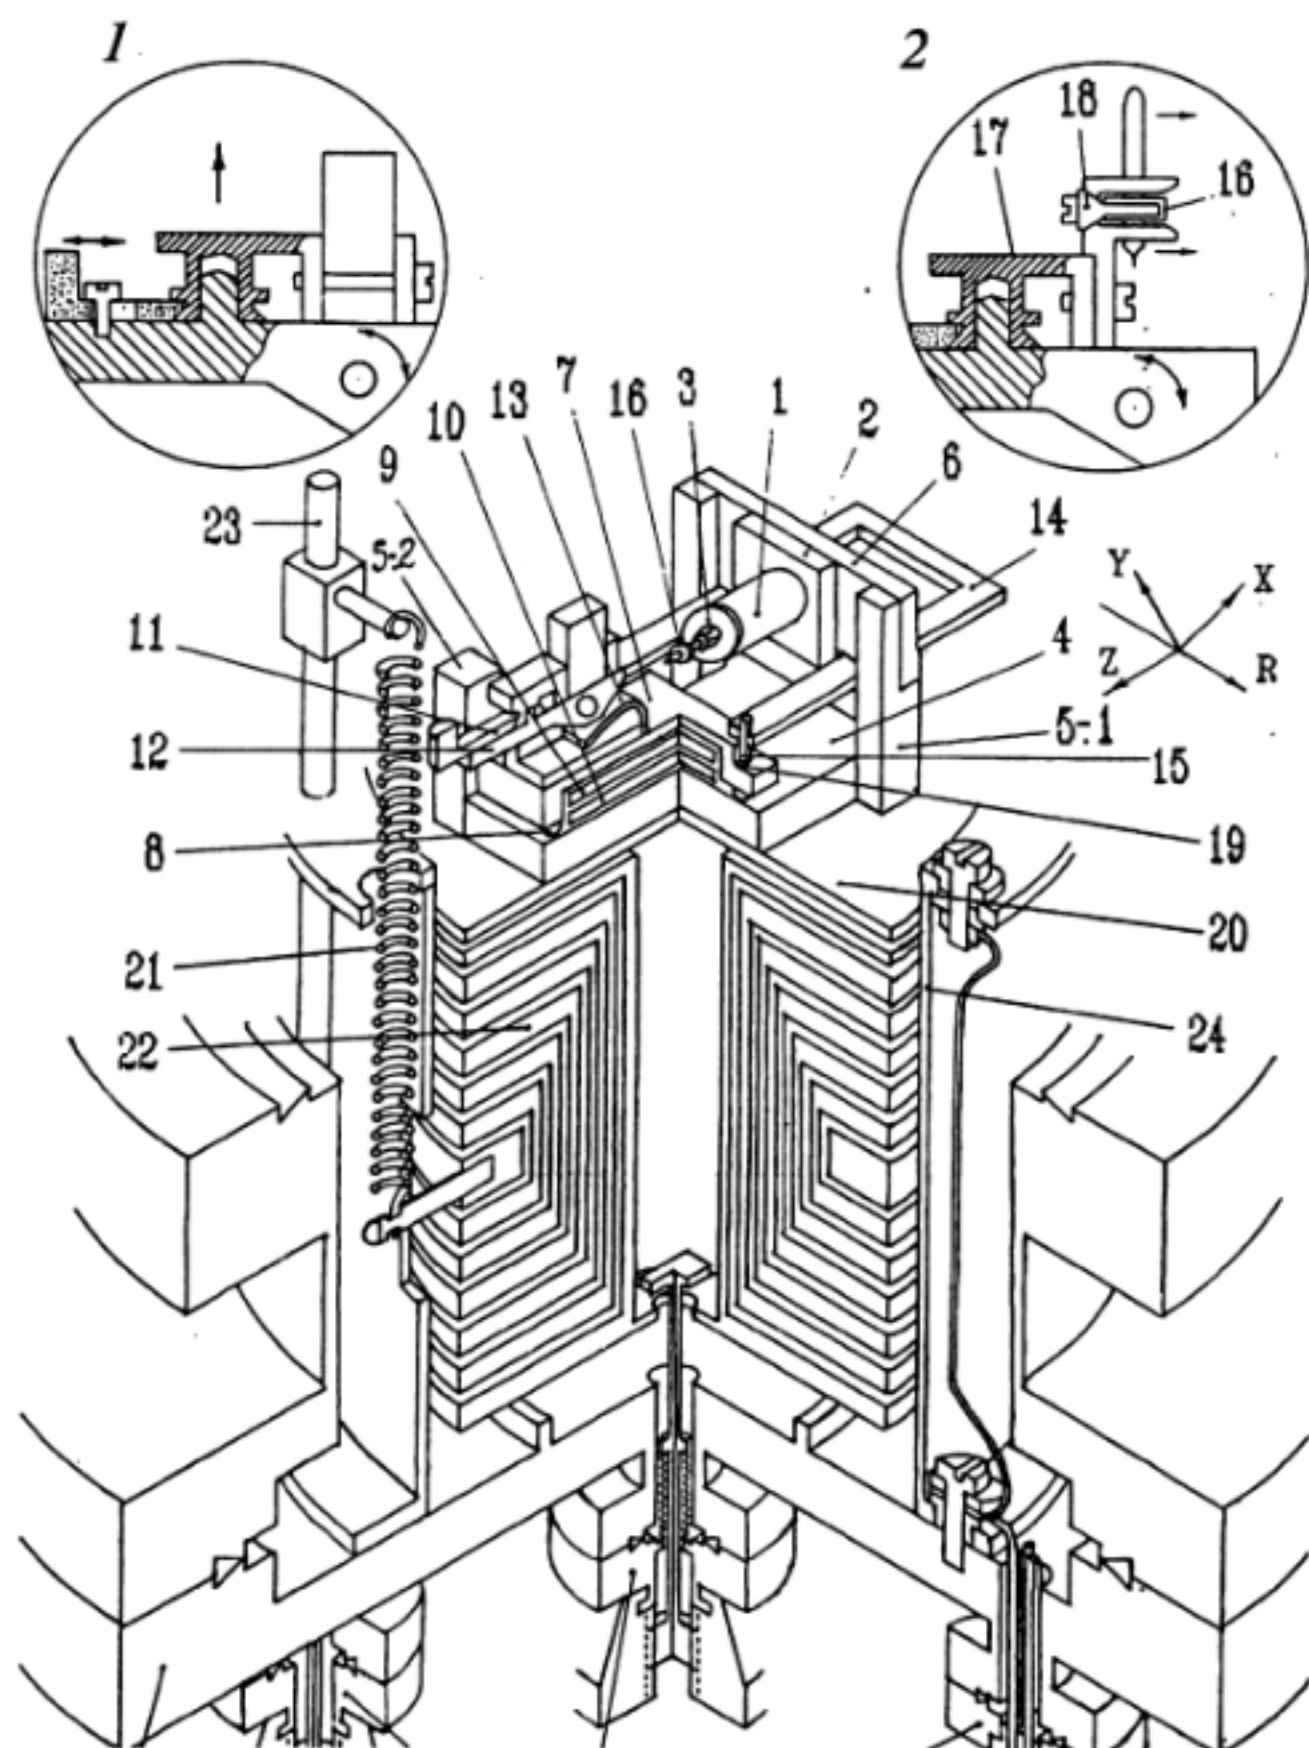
Конструкция сверхвысоковакуумного СТМ. Фрагмент 1 – держатель образца; фрагмент 2 – носитель острия
